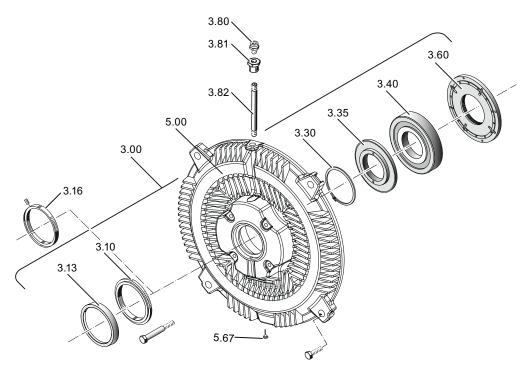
Mancal de rolamentos lado DE - Placa do mancal com tampa integrada
